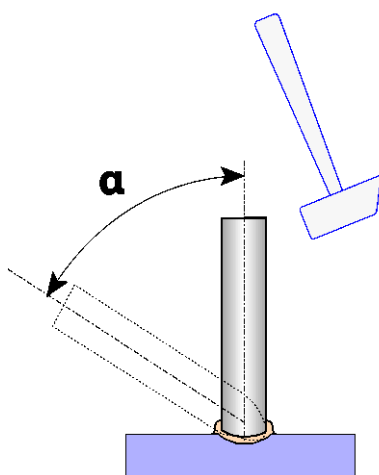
Sichtprüfung einer Bolzenschweißung
